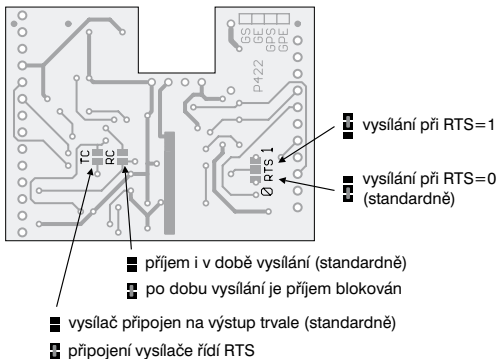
Převodník s modulem P232GS (EI5060.90)
